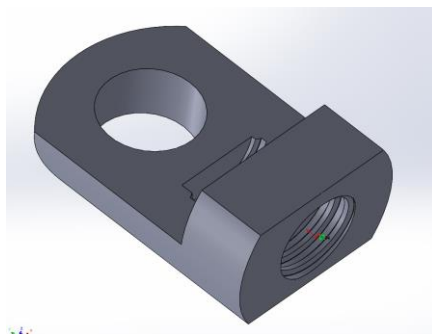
Кронштейн, один конец которого выполнен с отверстием, а другой конец - с резьбовым отверстием для установки на стержне.
